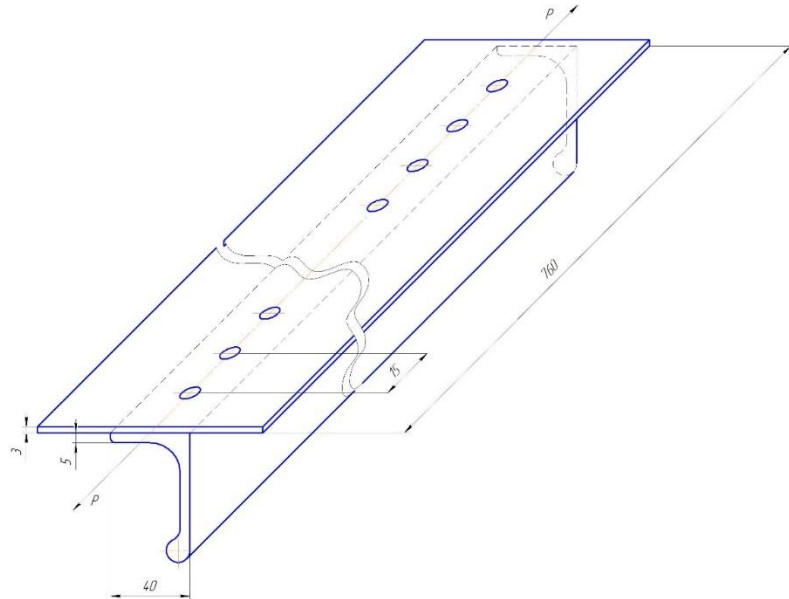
Розрахункова схема для з'єднання стрінгер-обшивки
